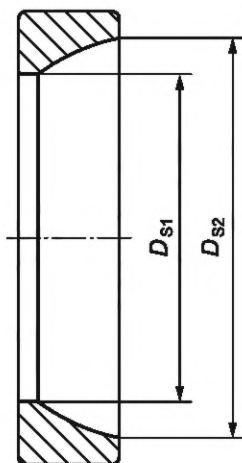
Наружное кольцо радиально-упорного шарнирного подшипника
